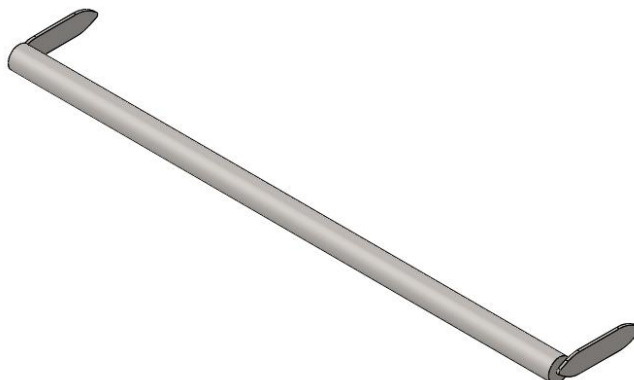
Diseño del eje principal en SolidWorks. Elemento real.
